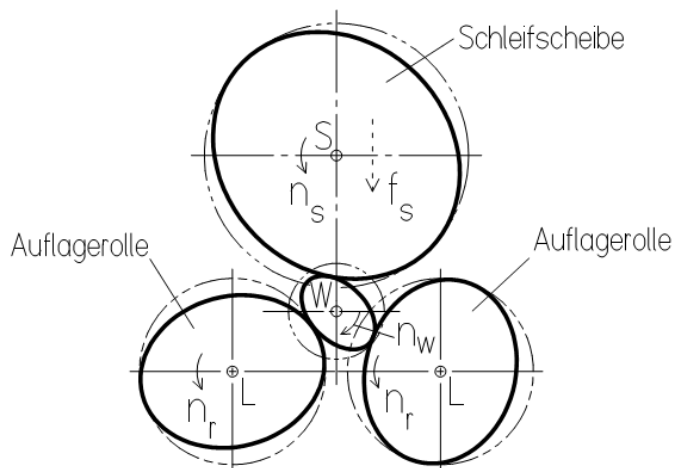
Spitzenlosschleifen eines Kolbenquerschnitts mit Verwendung von unrunder, synchron angetriebenen Auflagerrollen [ABL12a]
